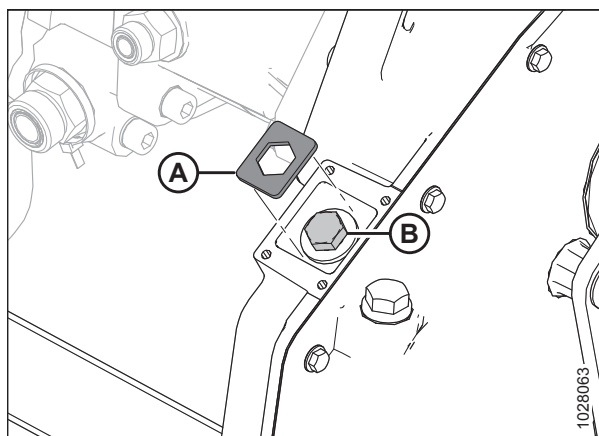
Hauptgetriebe mit Kettenspanner
